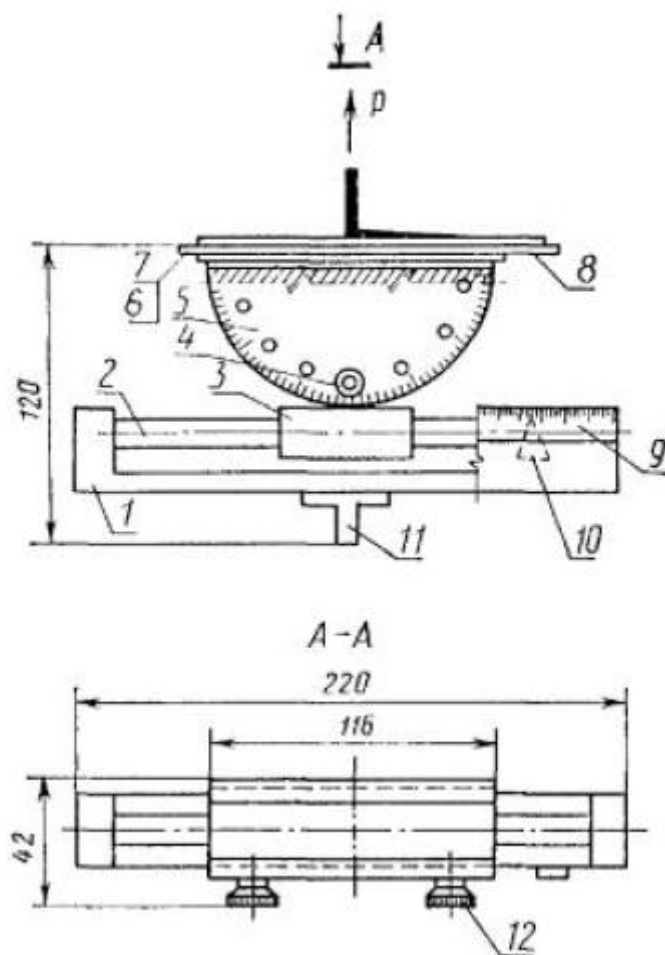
Пристрій для випробування під різними кутами: 1 – основа; 2 – напрямна; 3 – полозки; 4 – фіксатор; 5 – кутомір; 6, 7 – притискні гайки, планки та гвинти; 8 – зразок; 9 – лінійка; 10 – стрілка; 11 – перехід; 12 – затяжні гайки
